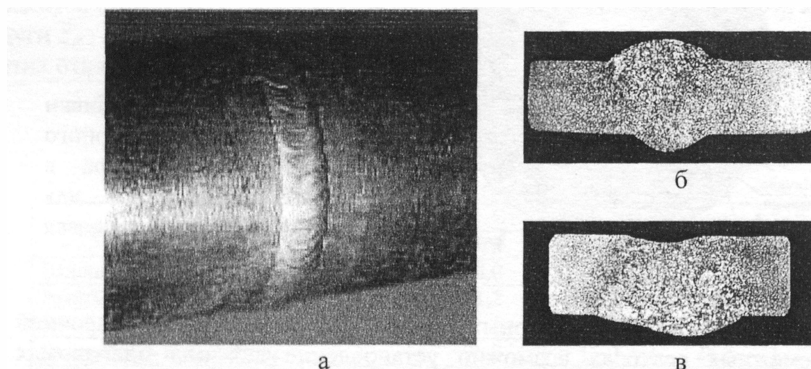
Формирование шва при орбитальной сварке труб диаметром 57×4 из стали 20 в U-образную разделку: а - внешний вид; б - макроструктура сварного шва при сварке в нижнем положении; в – при сварке в потолочном положении
